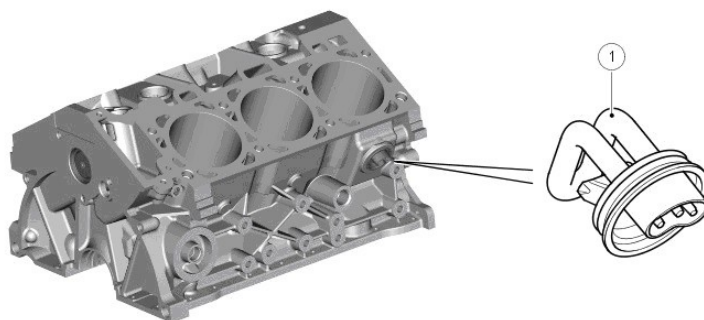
Подогреватель блока цилиндров бензинового двигателя 4.0L V6
